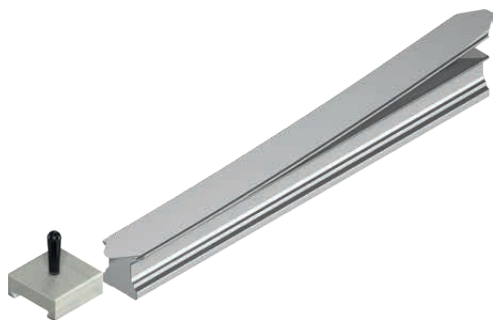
Montage Abdeckband mit Montagewerkzeug
